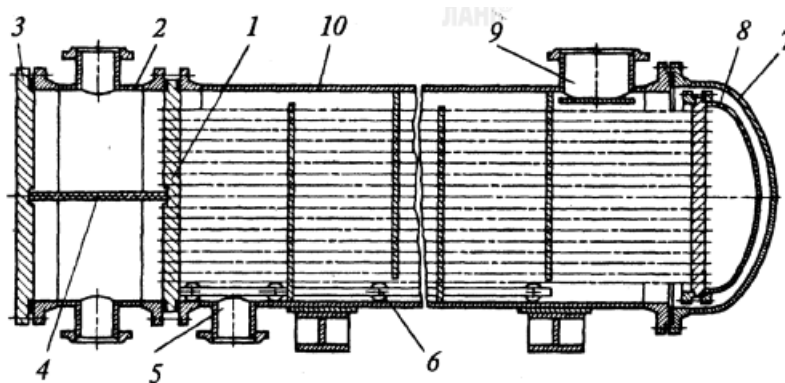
Кожухотрубчатый теплообменник с плавающей головкой
